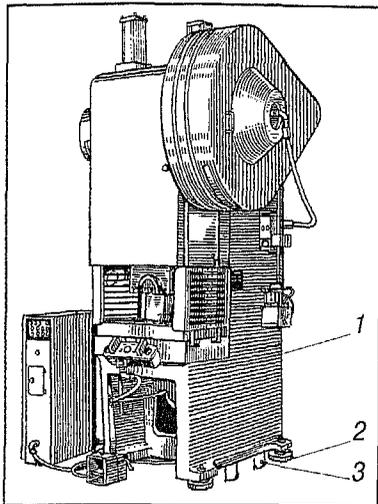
Конструктивная схема виброизолирующей установки листоштамповочного пресса:
